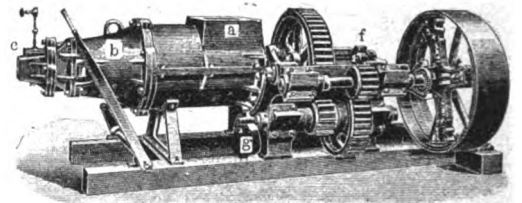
Ziegelpresse „Giant Auger Machine.“
